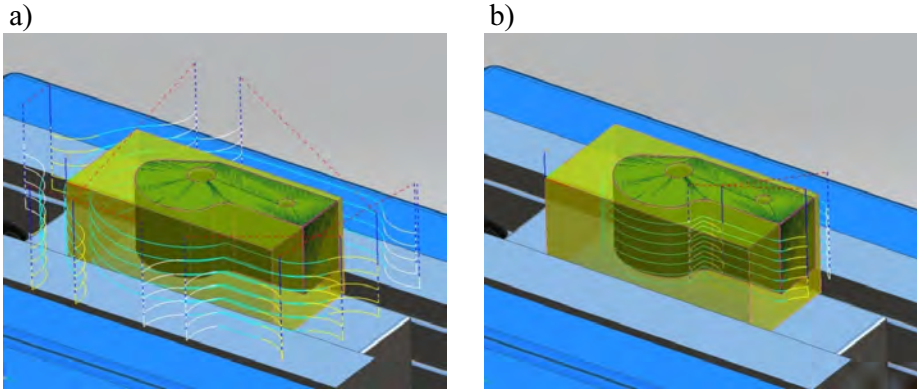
Złożenie modelu i wskazanie geometrii WORKPIECE
